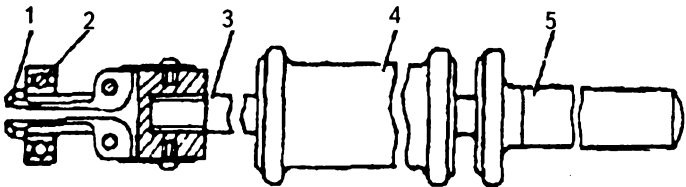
Съемник для выпрессовки подшипника из коленчатого вала:
